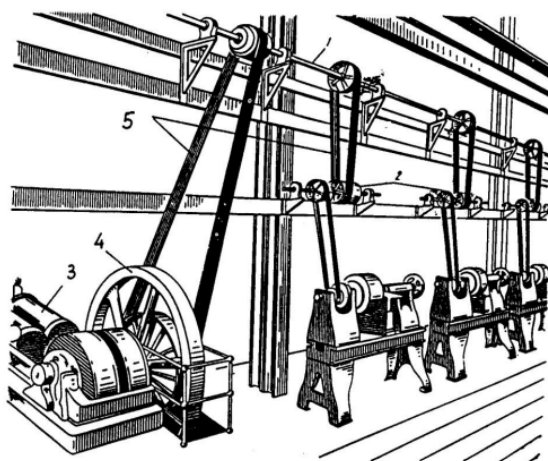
Схема группового привода: 1 – трансмиссионный вал; 2 – контрприводы; 3 – паровая машина; 4 – маховик; 5 – ремень
